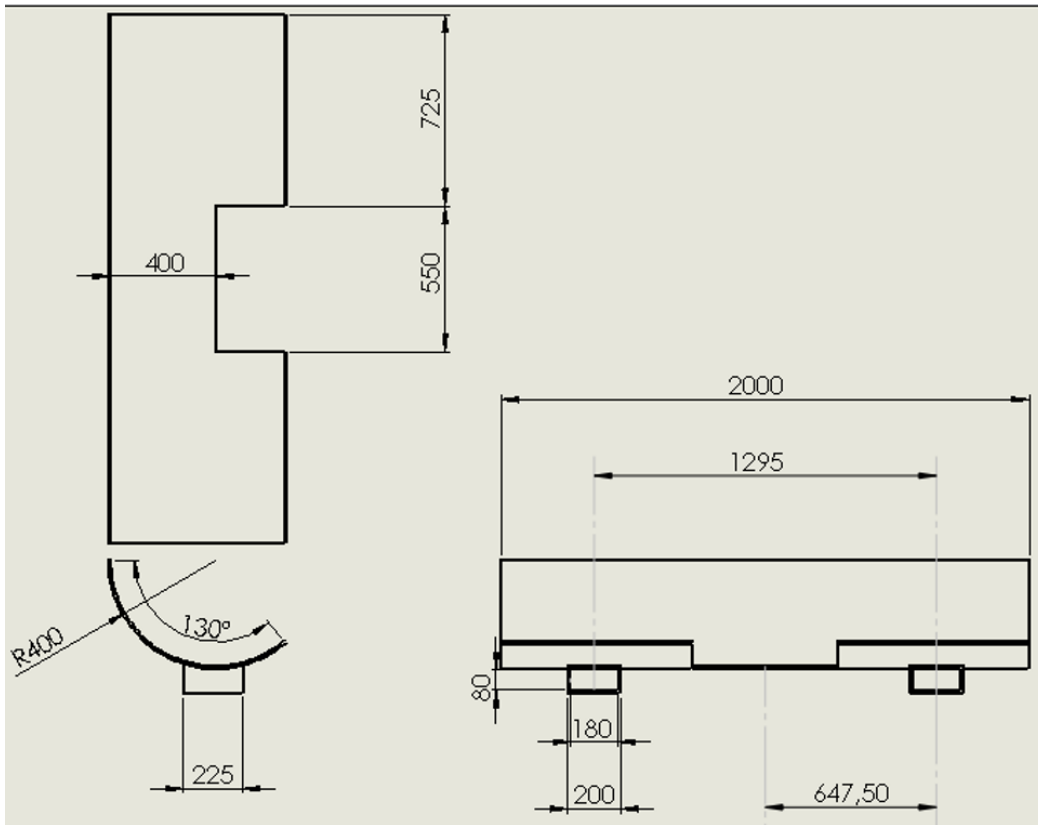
Disegno quotato struttura di stoccaggio bobina
